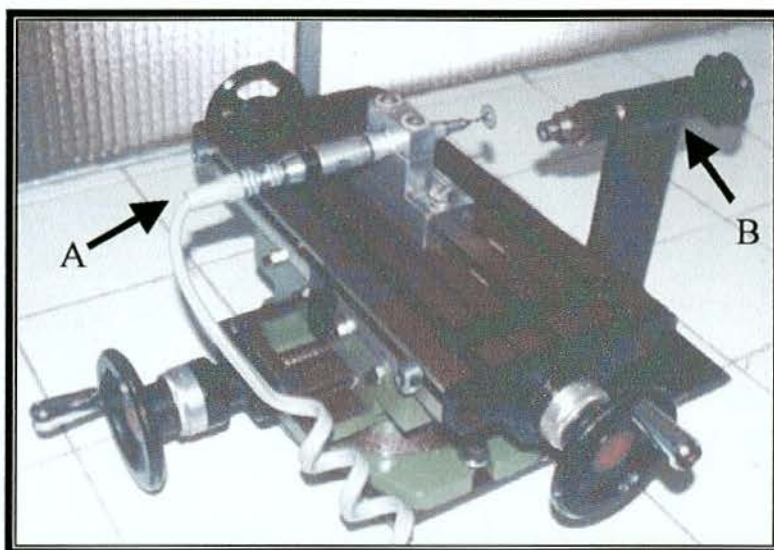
Aparelho adaptado para realização dos cortes: a) conjunto peça reta e disco fixado sobre mesa de coordenadas; b) mandril de fixação dos materiais a serem cortados.
